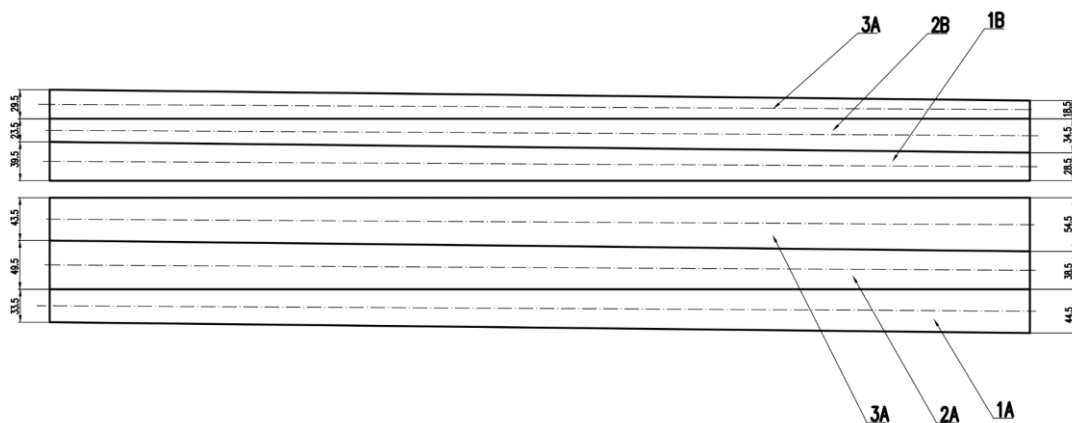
Úprava rozměrů formy na CNC frézce
